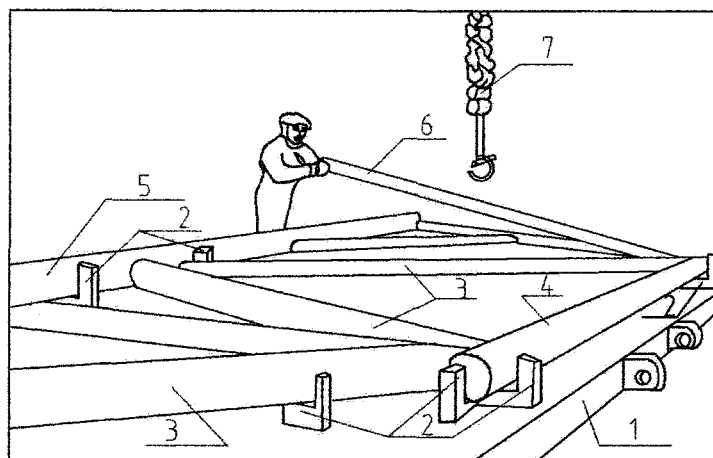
Сборки фермы из труб на Челябинском заводе металлоконструкций: 1 – плита-ростверк; 2 – упоры; 3 – раскосы; 4 – пояс нижний; 5 – пояс верхний; 6 – устанавливаемый раскос; 7 – строп мостового крана
